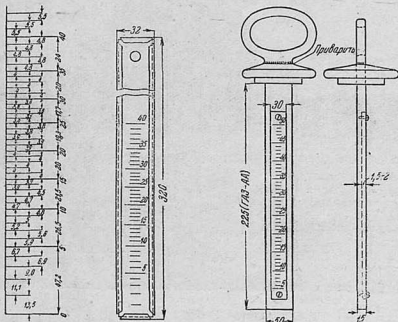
Линейка для замера бензина. Слева — разметка шкалы линейки для автомобилей ГАЗ-АА
